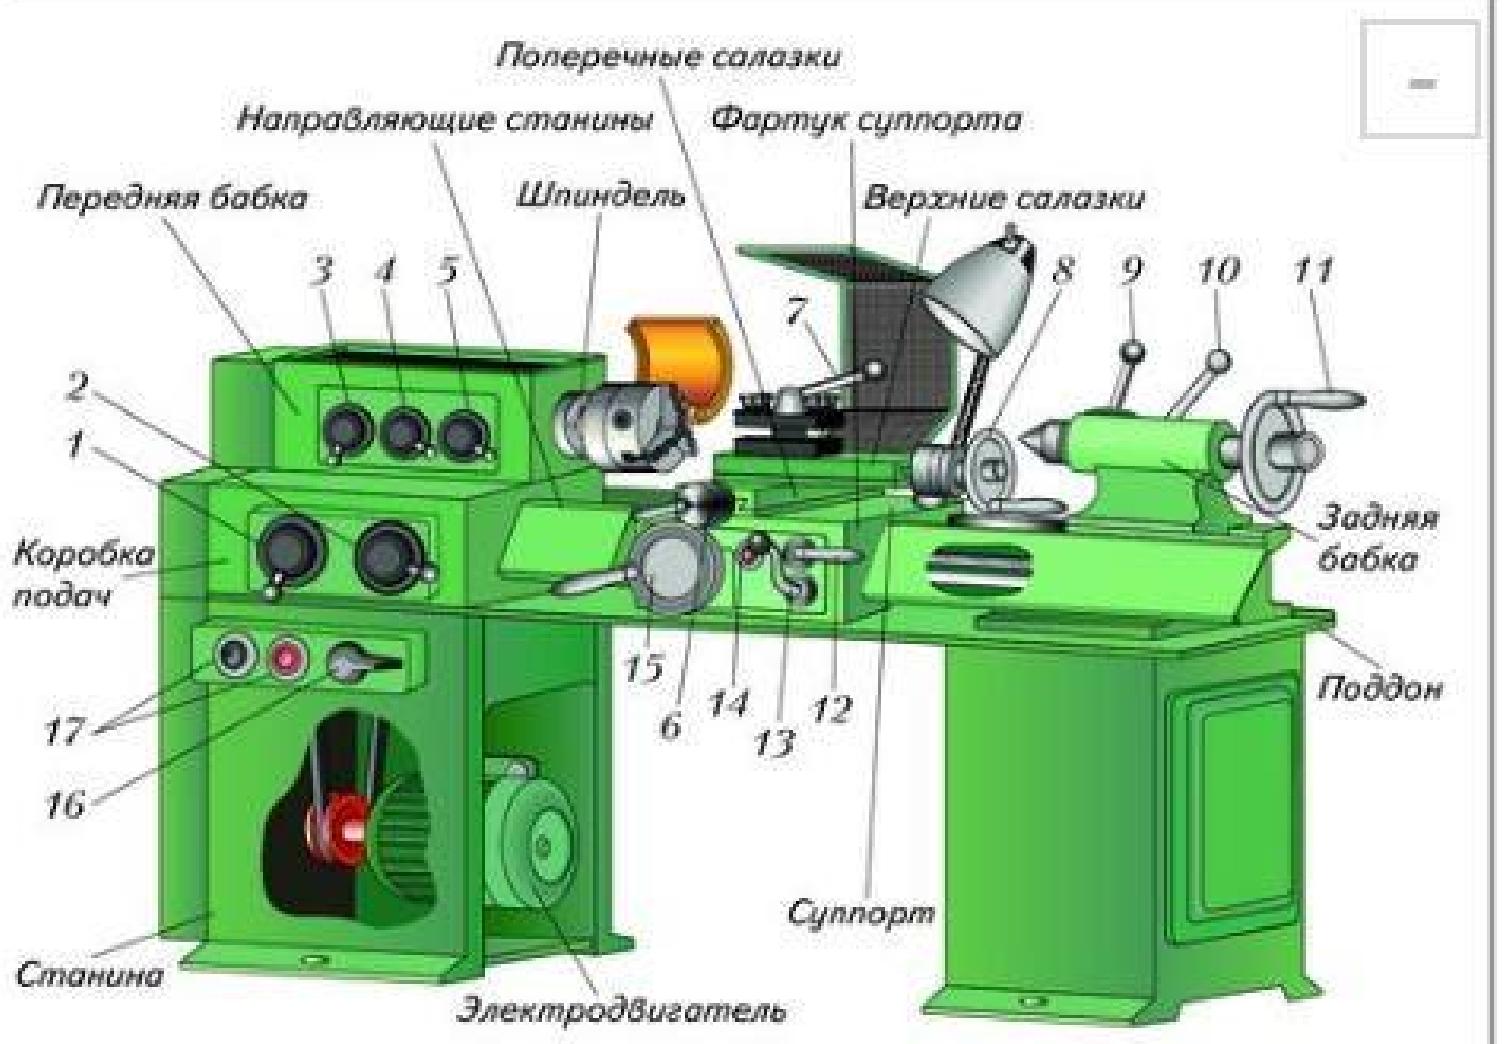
Токарно-винторезный станок ТВ-6: 1, 2 – рукоятки переключения величины подачи; 3 – рукоятка переключения гитарного механизма; 4, 5 – рукоятки переключения частоты вращения шпинделя; 6 – рукоятка поперечной подачи суппорта; 7 – рукоятка закрепления резцодержателя; 8 – рукоятка перемещения верхних салазок; 9 – рукоятка крепления шиноли; 10 – рукоятка крепления задней бабки; 11 – маховик подачи шиноли; 12, 13 – рукоятки управления механической подачей; 14 – кнопка включения реечной передачи; 15 – маховик перемещения суппорта; 16 – рукоятка реверса; 17 – кнопки включения и отключения электродвигателя
